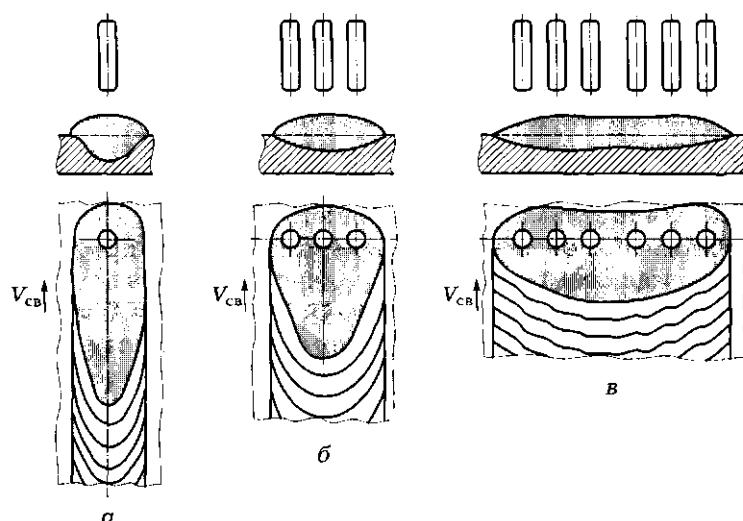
Формы сварочной ванны и глубина проплавления при наплавке одним (а), тремя (б) и шестью (в) электродами (стрелками показаны направления наплавки)
